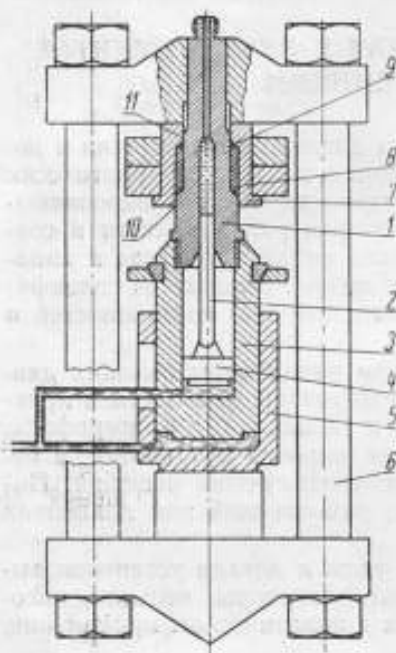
Схема мультипликатора с внешней поддержкой цилиндра, осуществляемой сжатием уплотнения
